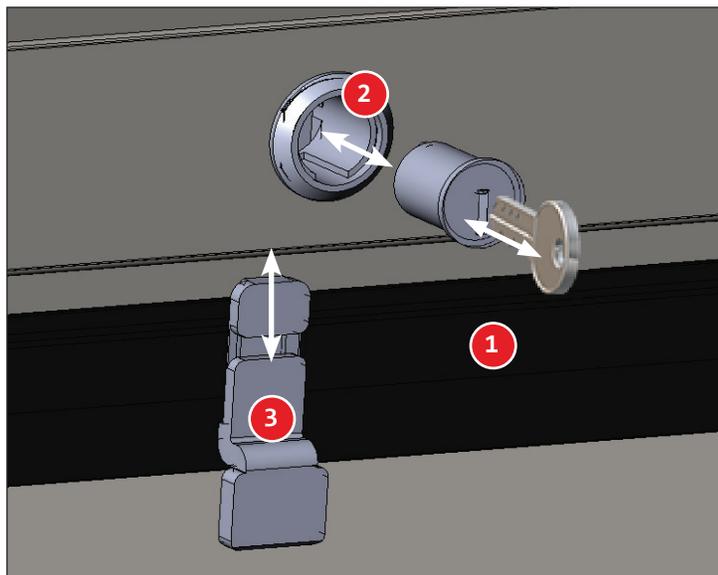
Vista frontal del desmontaje/montaje de los componentes.
